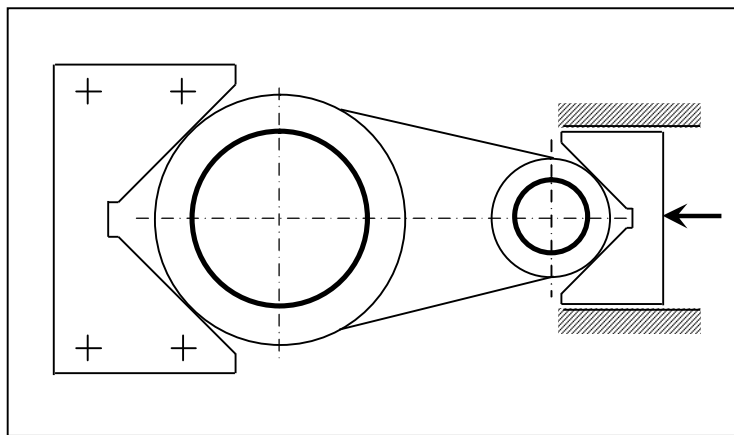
Спрощена конструктивна схема верстатного пристрою
